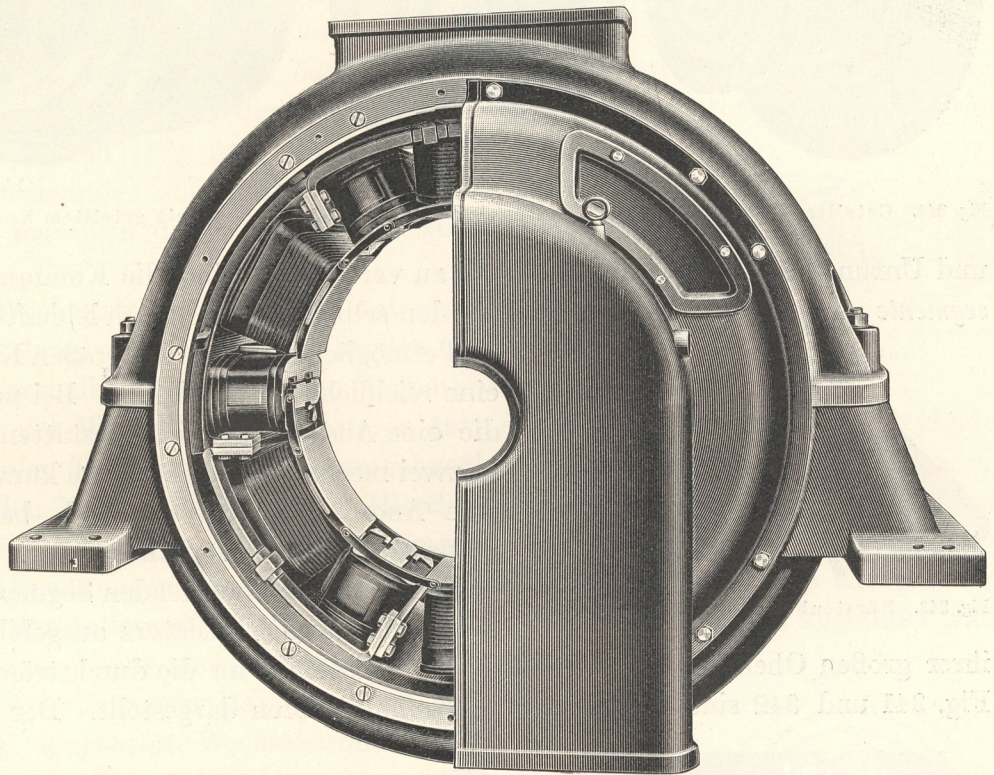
Magnetgestell und Gehäuse eines Gleichstrom-Turbogenerators mit Wendepolen.
